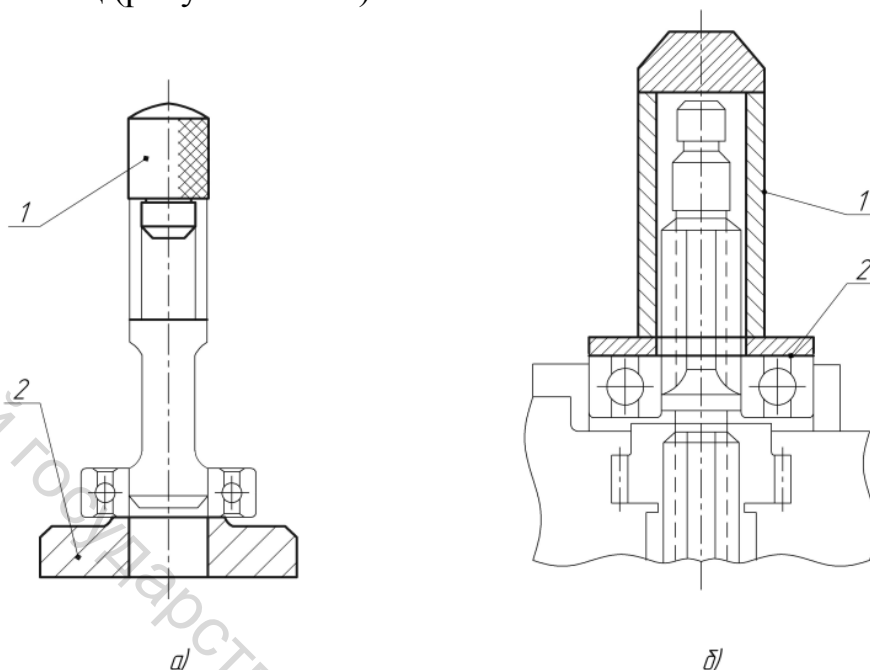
Схемы установки подшипников качения на валу и в корпусе
